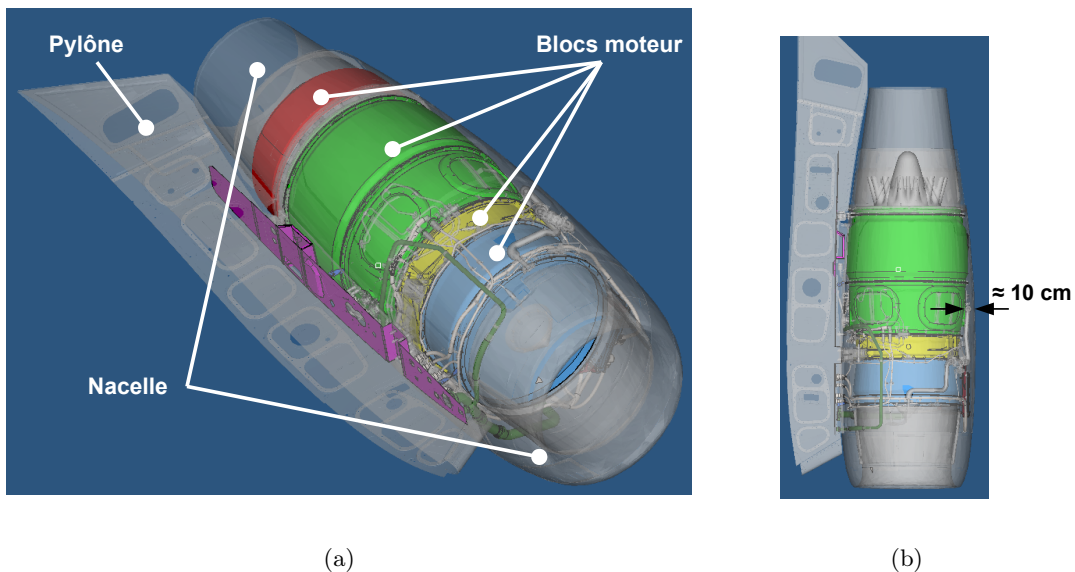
Géométrie globale du moteur latéral gauche (a) et vue de dessus (b)
